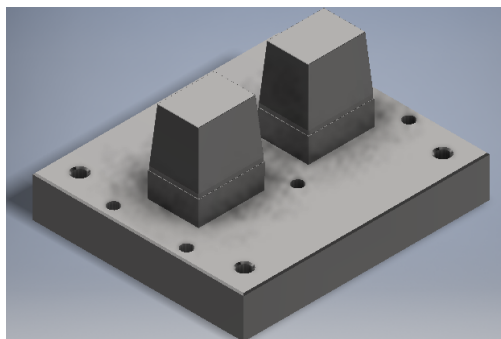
Placas portamolde de macho de moldeo con sus respectivos machos de moldeo.
